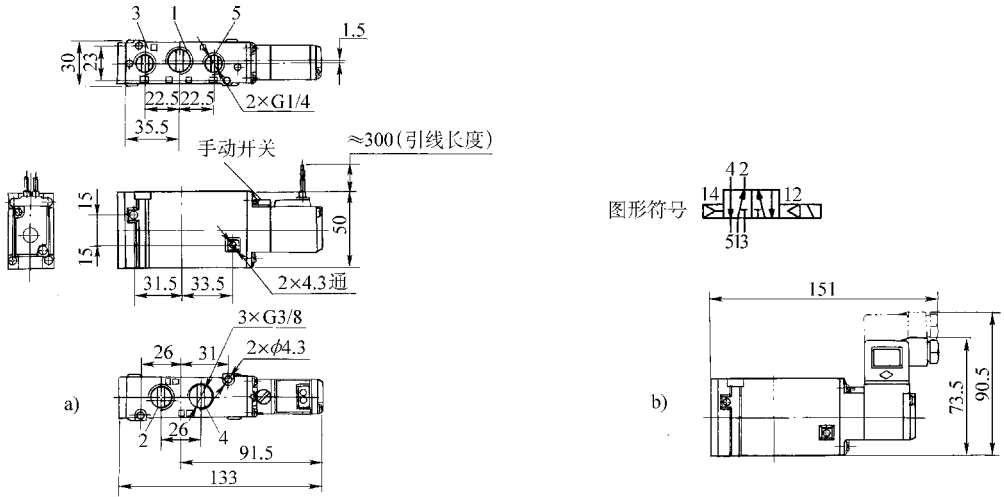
VFS3000 系列硬质(金属)密封二位、三位五通先导式电磁换向阀外形尺寸
